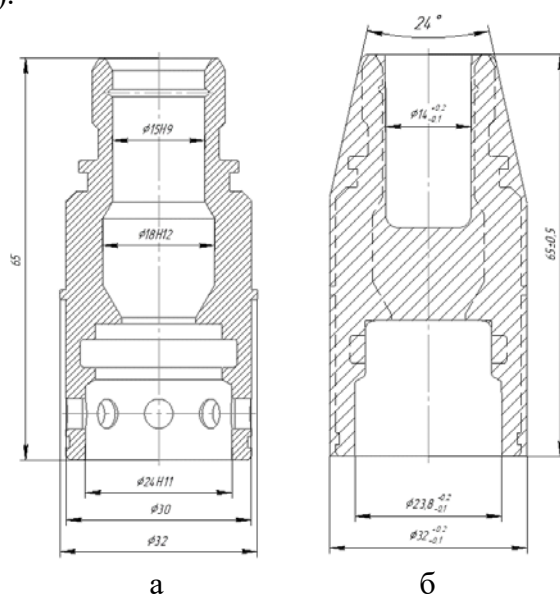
Эскиз детали гидромуфты «Корпус левый»:
